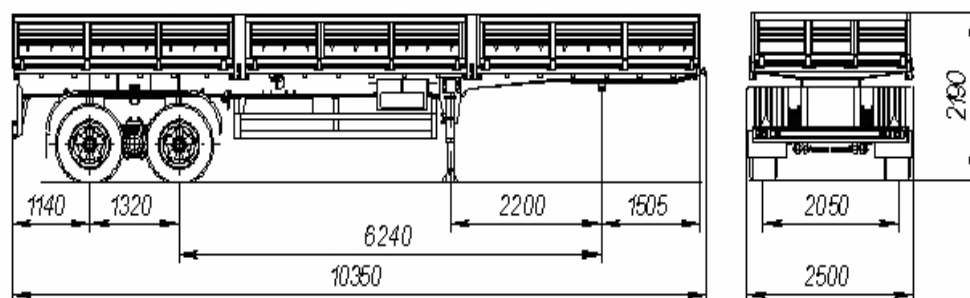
Схема полуприцепа автомобильного НЕФАЗ – 9334-0000010-11.
